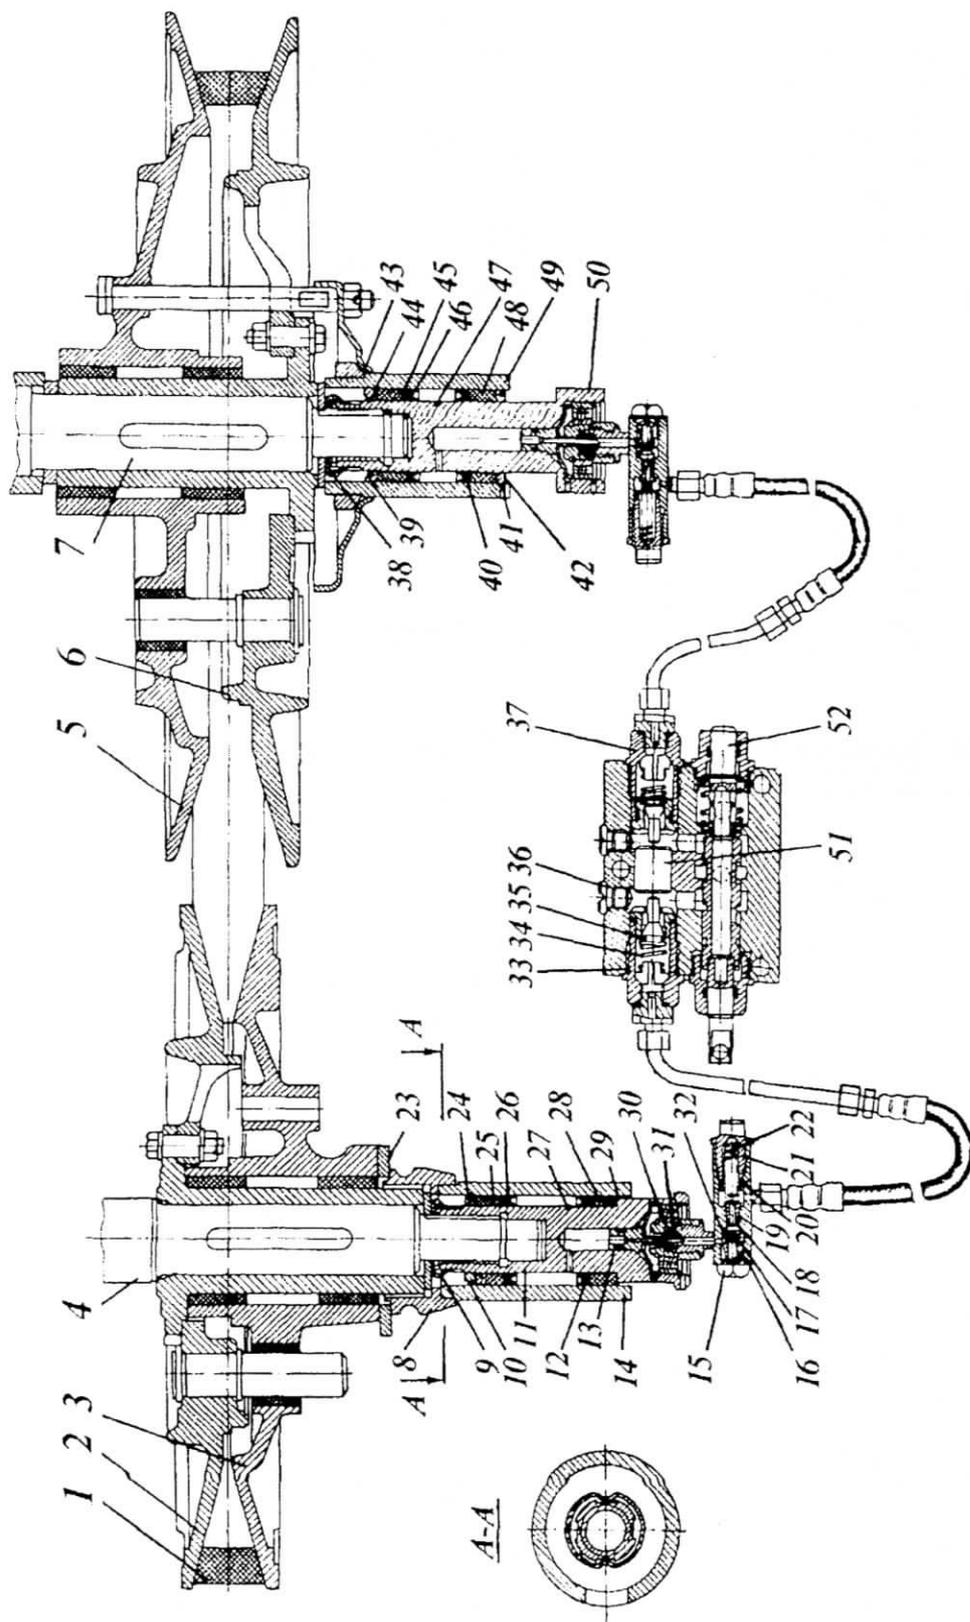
Вариатор молотильного барабана с гидроцилиндрами:
